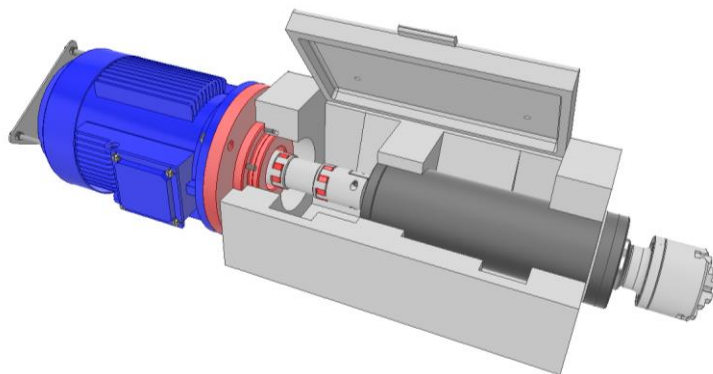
Конструкция прямого привода главного движения станка ТПК-125BM
